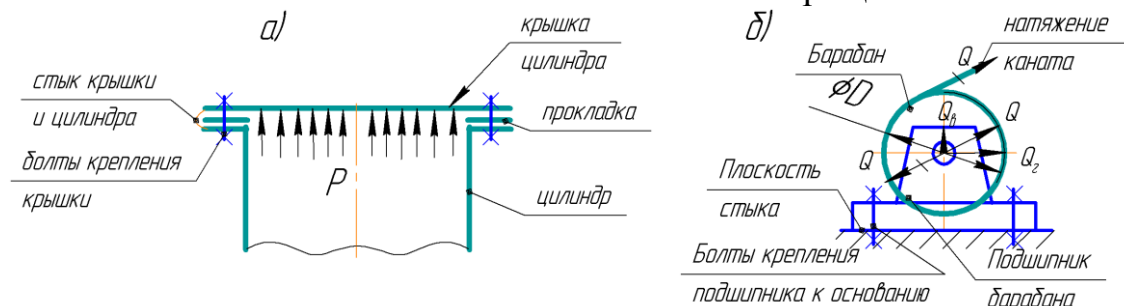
Ситуации, приводящие к нагружению болтов центральной отрывающей силой: а) крепление крышки цилиндра; б) крепление подшипников барабана
